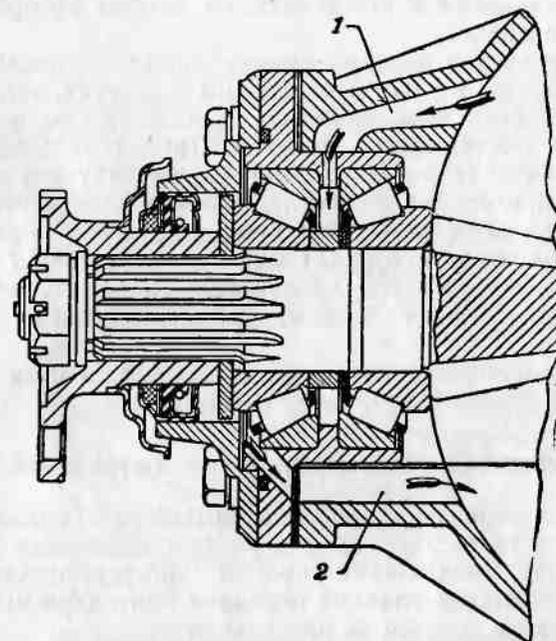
Схема смазки переднего подшипника ведущей шестерни главной передачи:
